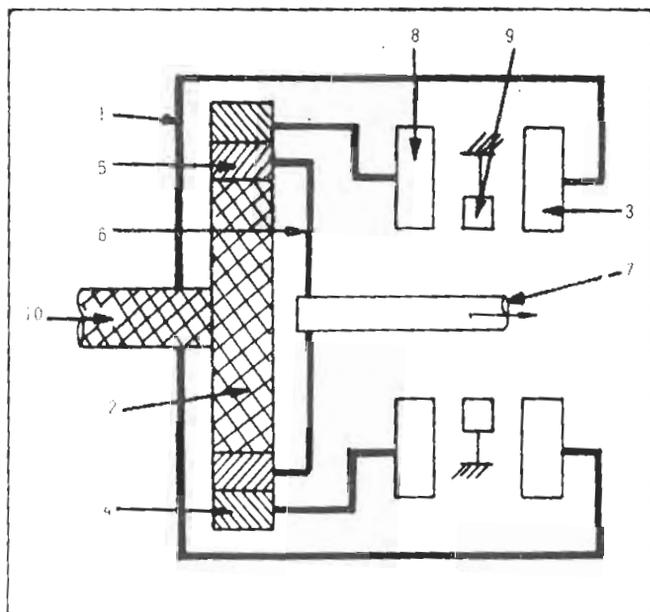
Esquema del divisor de par. 1.- Volante. 2.- Planeta. 3.- Impulsor. 4.- Corona. 5.- Satélite. 6.- Portasatélites. 7.- Eje de salida. 8.- Turbina. 9.- Estátor. 10.- Cigüeñal.
